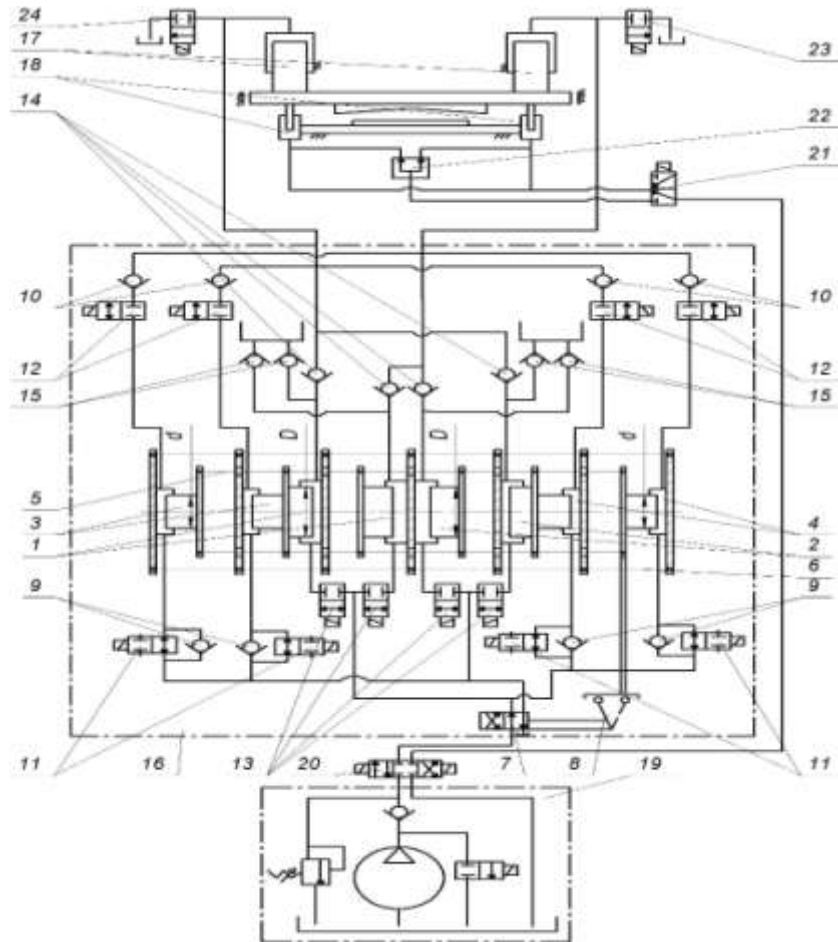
Схема привода с блочным редуктором–мультипликатором непрерывного действия
